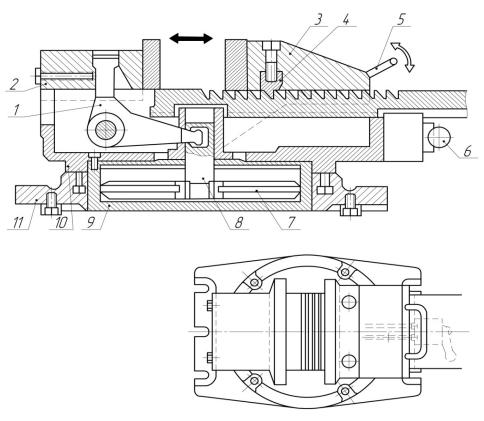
Пневматические быстропереналаживаемые тиски: 1 – рычаг; 2 – подвижная губка; 3 – неподвижная губка; 4 – планка; 5 – рукоятка; 6 – распределительный кран; 7 – поршень; 8 – шток; 9 – пневмоцилиндр; 10 – поворотный корпус; 11 – основание
